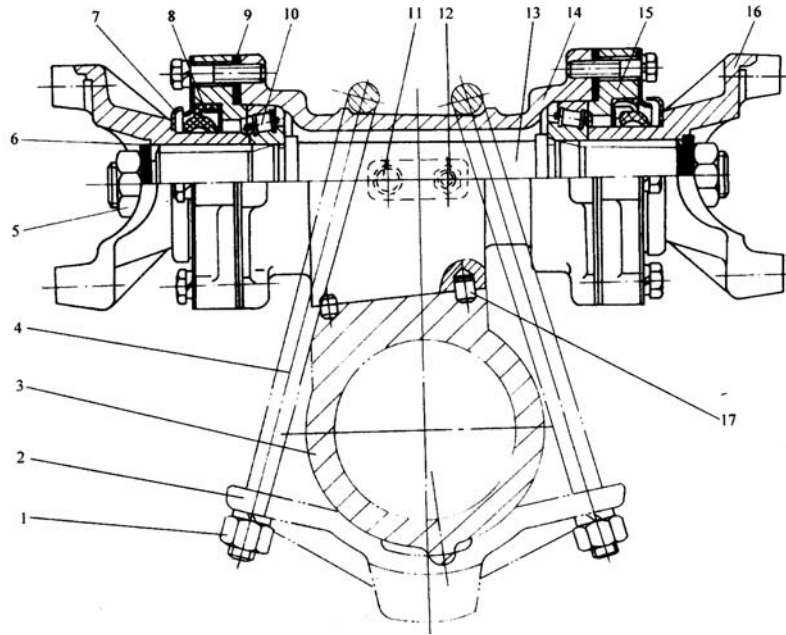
东风 EQ2080 型汽车传动轴中间支承
